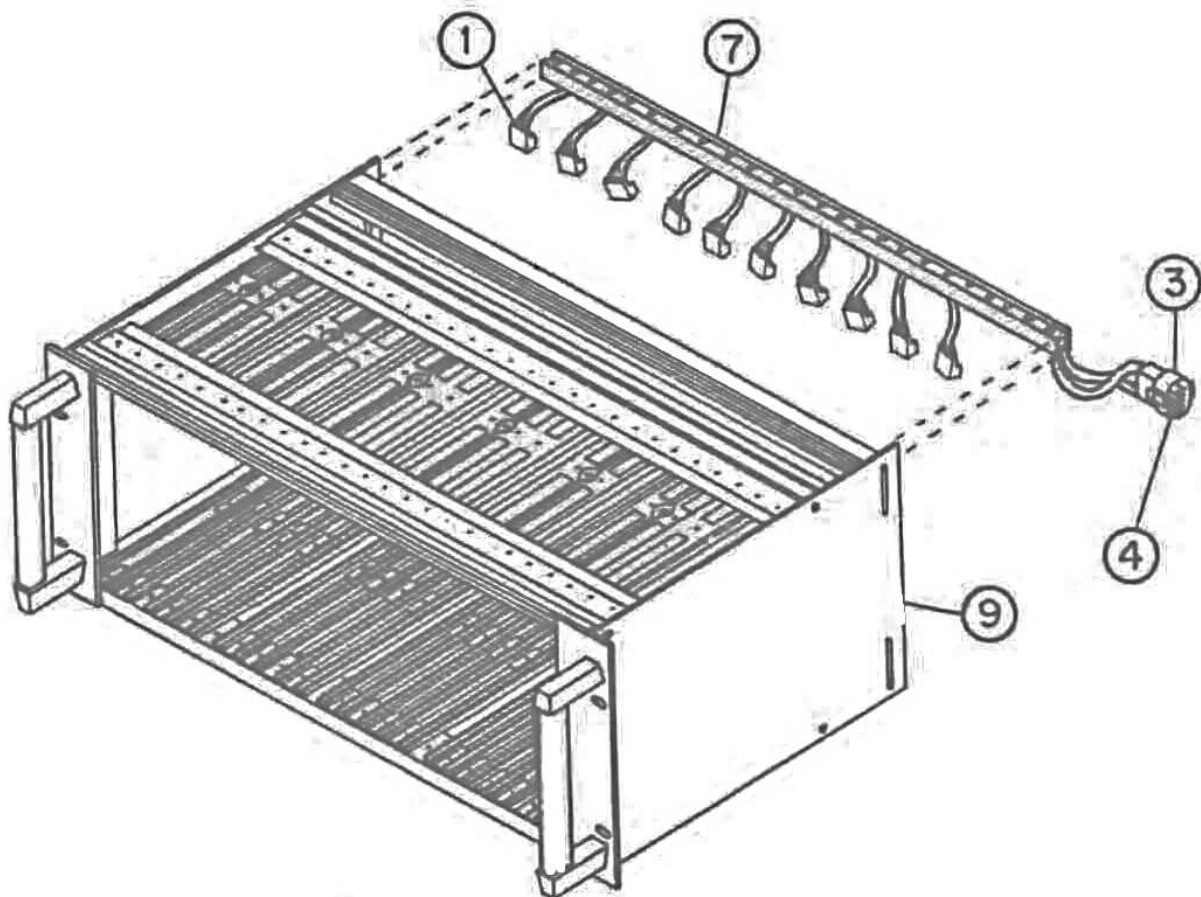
Estrutura SUB-4U-XX-1 - vista explodida
